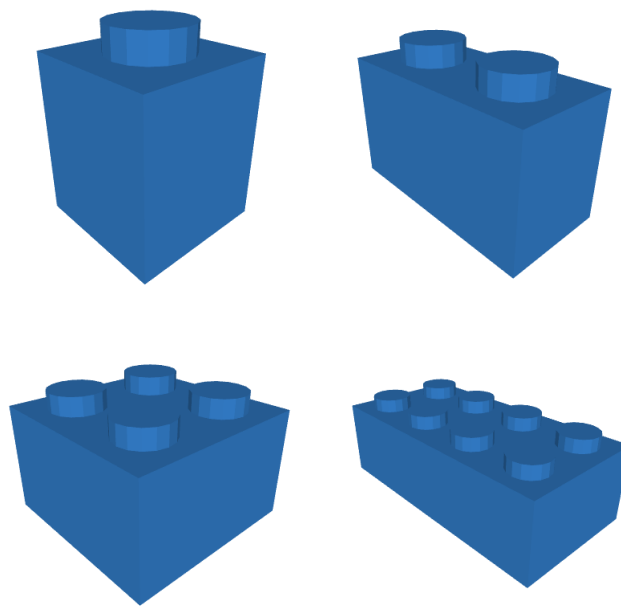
Brick 1x1, 1x2, 2x2 e 2x4. Modelos STL destas peças estão disponíveis em Anexo.
